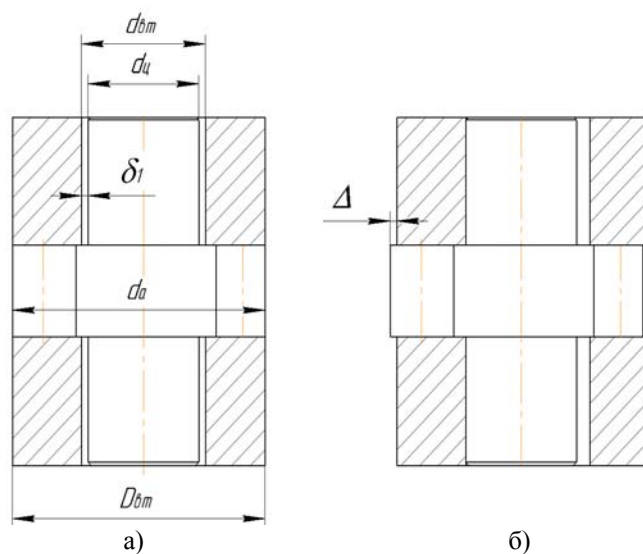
Схема взаємного розташування деталей шестеренного насоса
